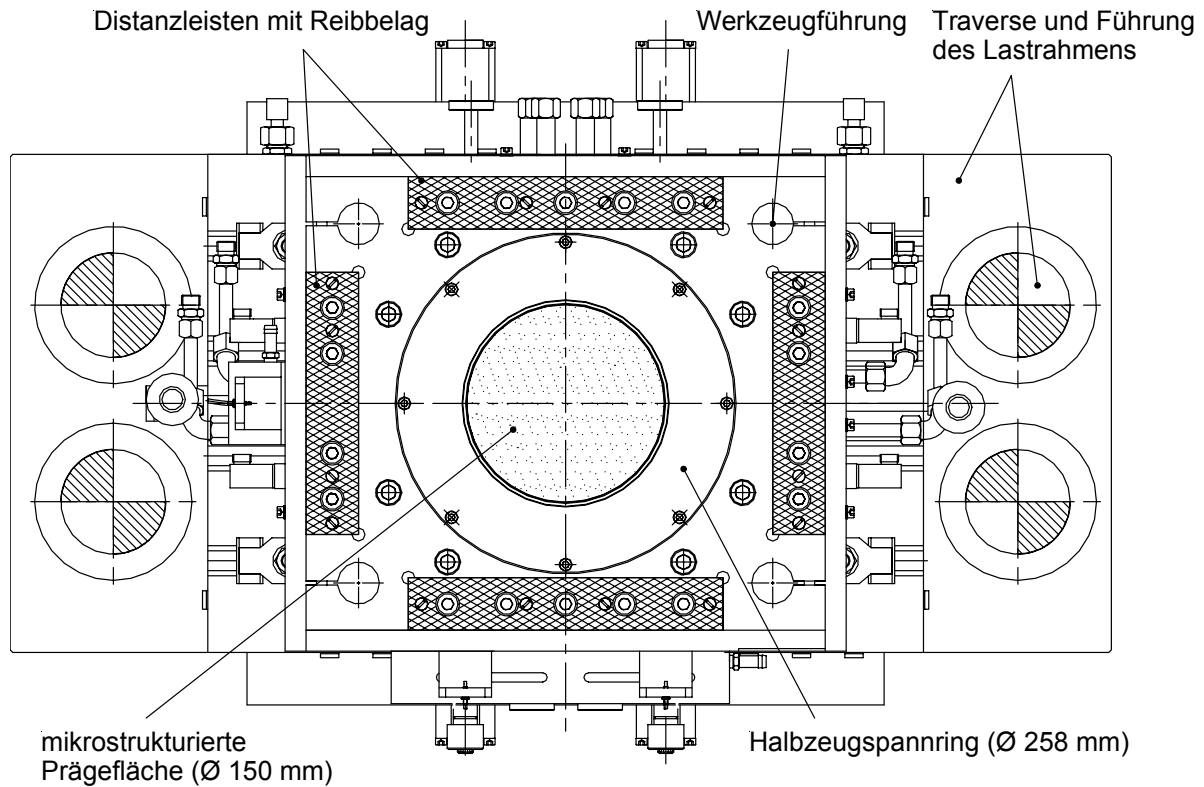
Aufsicht der unteren Werkzeughälfte (siehe Abb. 5-1, Schnitt A)
